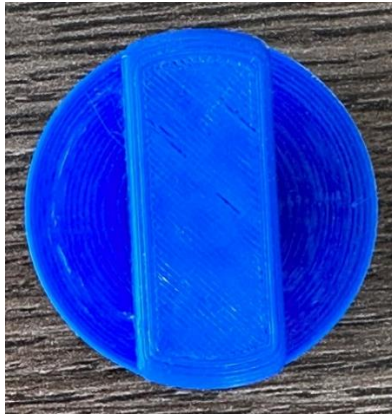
Perilla de Calefacción impresa con 3D (PLA)
